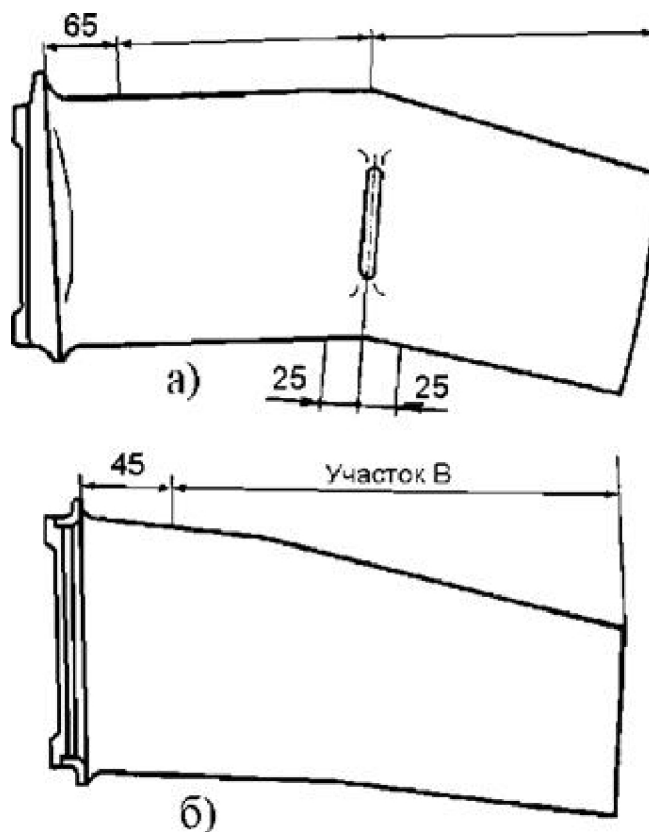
Рабочие лопатки первой (а) и второй (б) ступени ротора НД
